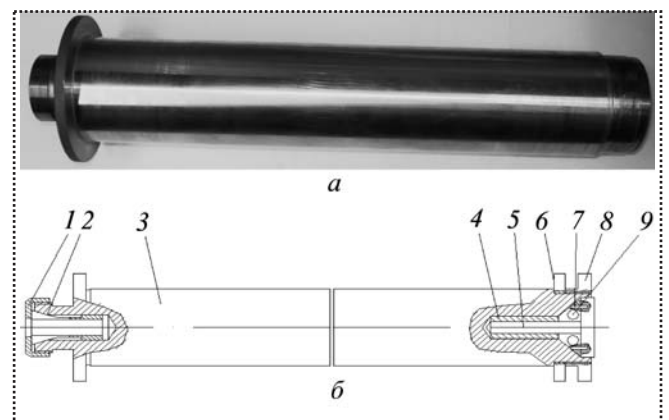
Внешний вид (а) и конструкция (б) шпинделя
